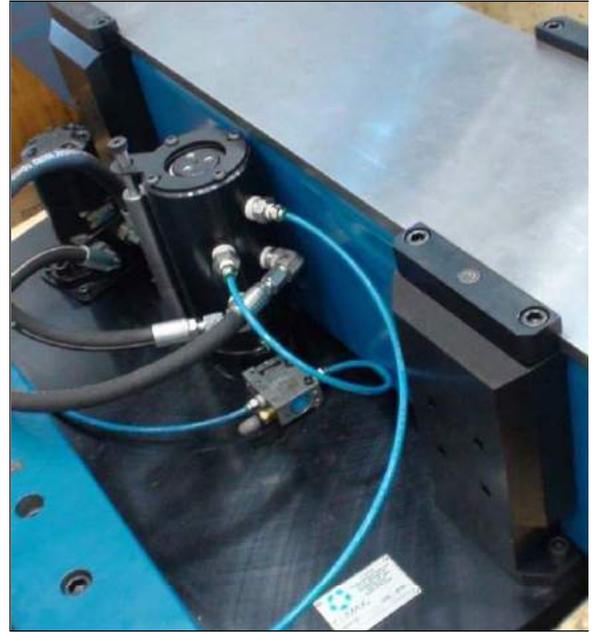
CONFIGURACIÓN DE MONTAJE OD
